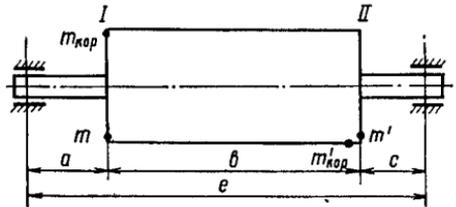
Схема динамической балансировки ротора на резонансном станке
